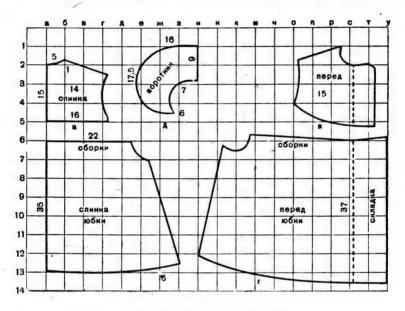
Чертёж деталей платья: a — спинка кокетки;  $\delta$  — спинка юбки;  $\theta$  — перёд кокетки;  $\epsilon$  — перёд юбки;  $\theta$  — воротник.
